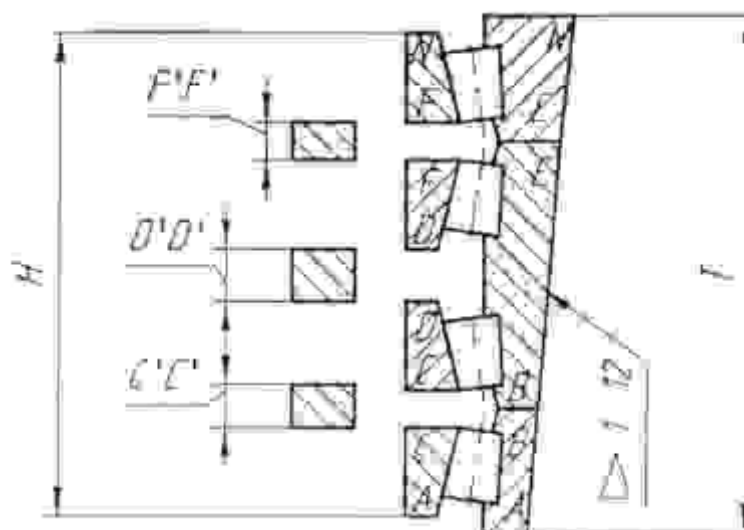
Схема установки деталей подшипника серии 577000 в подушку.
